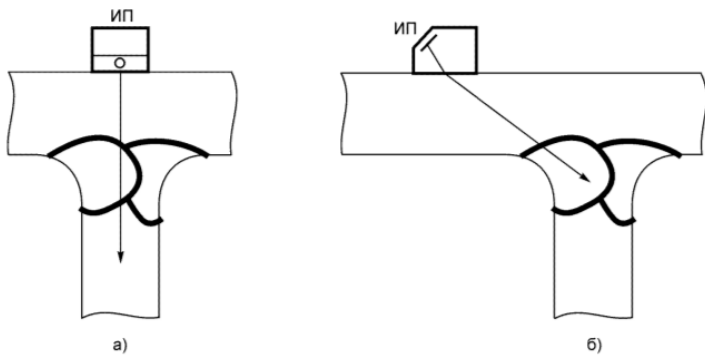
Схемы прозвучивания таврового сварного соединения прямым лучом
